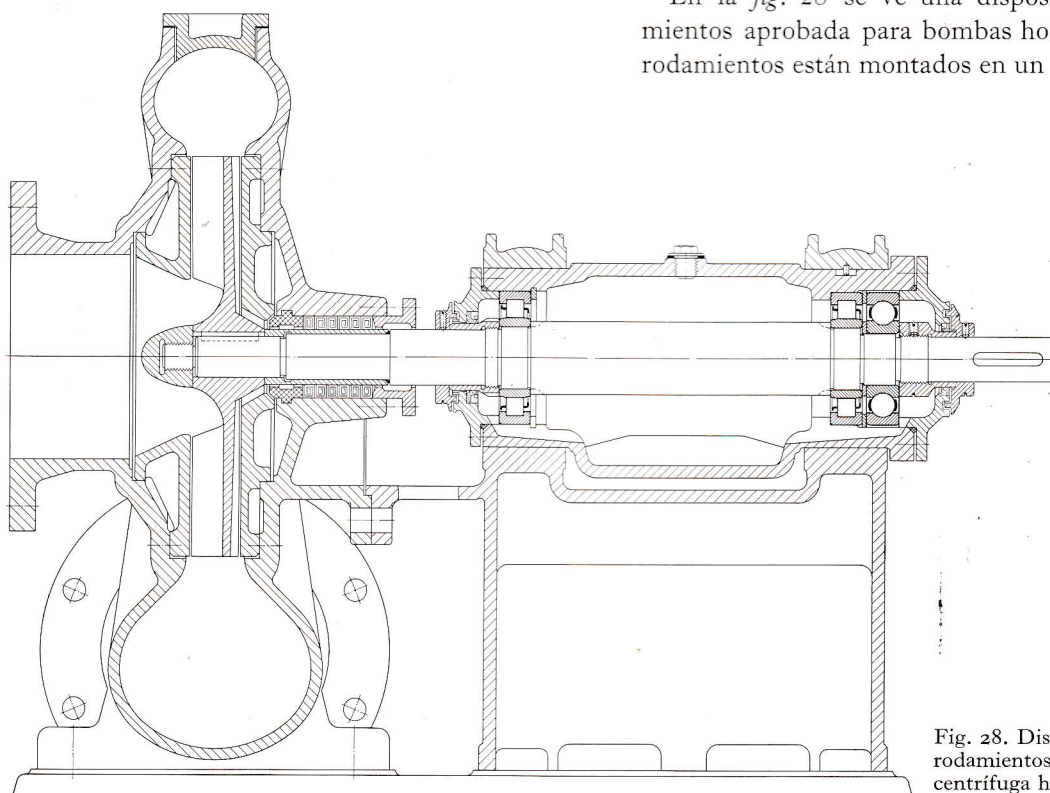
Disposición de rodamientos de una bomba centrífuga horizontal
